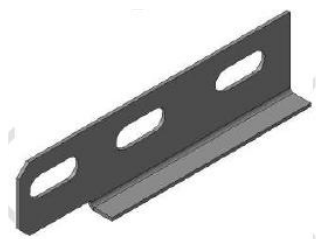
Соединитель вертикальный лотка лестничного лотка (1,2) ПжТехКабель
